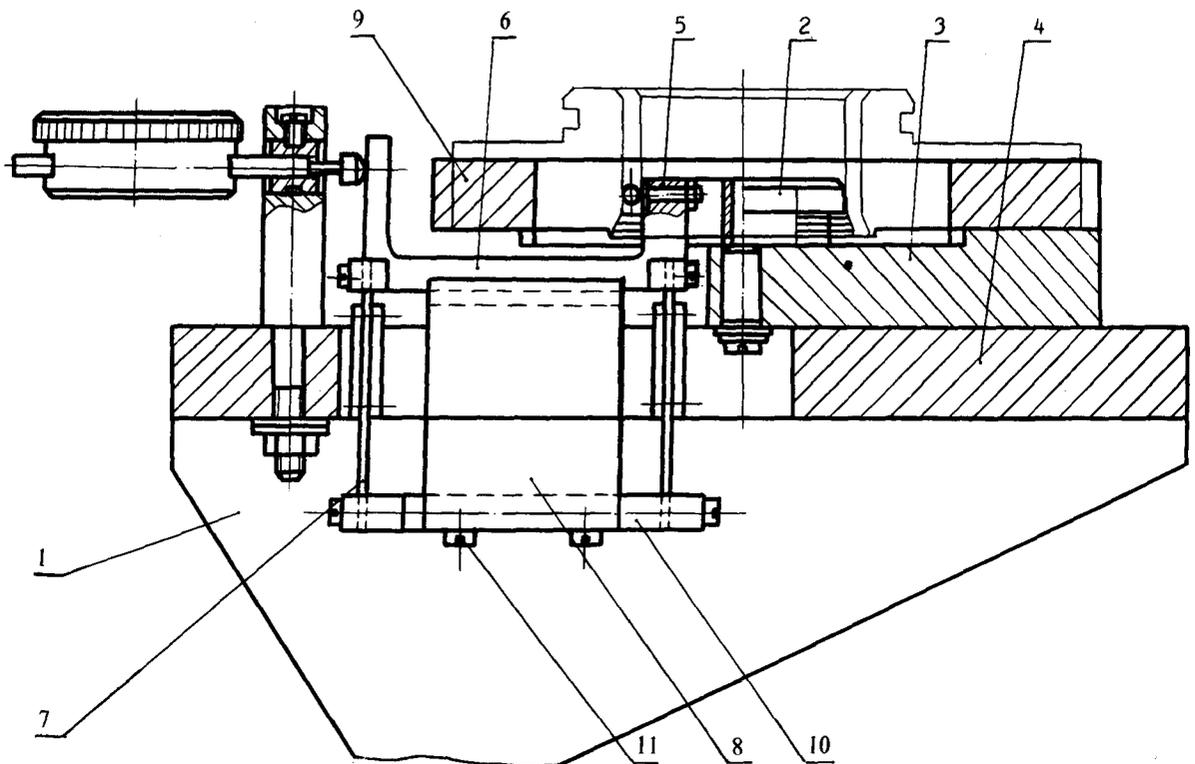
Приспособление для контроля шлицевого отверстия:
